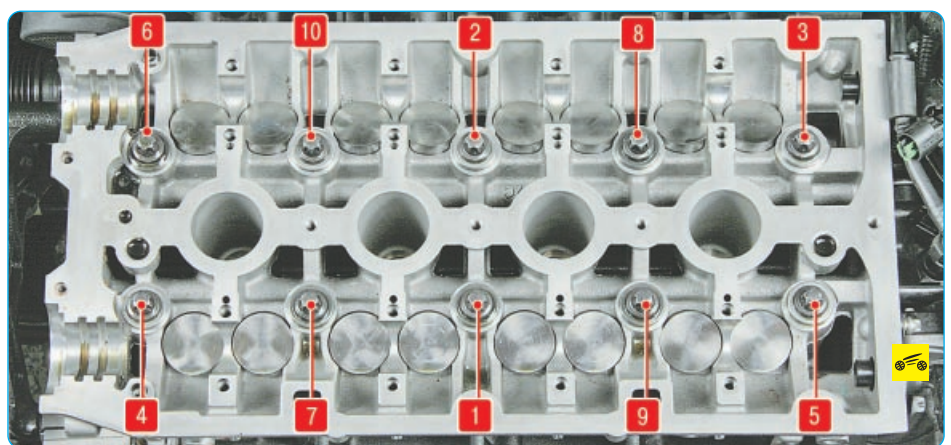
Порядок вворачивания болтов крепления головки блока цилиндров
